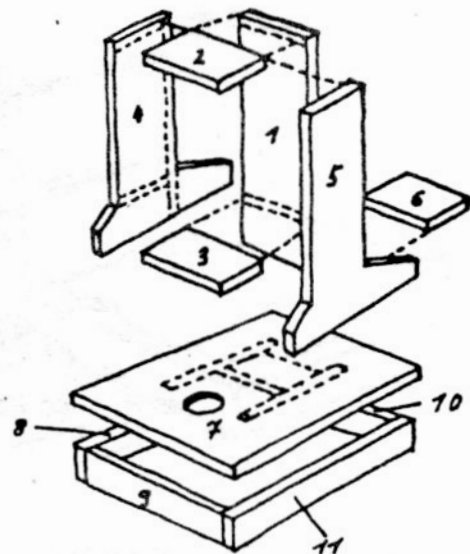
Aussäge-Skizze und Explosionszeichnung des Turmes
